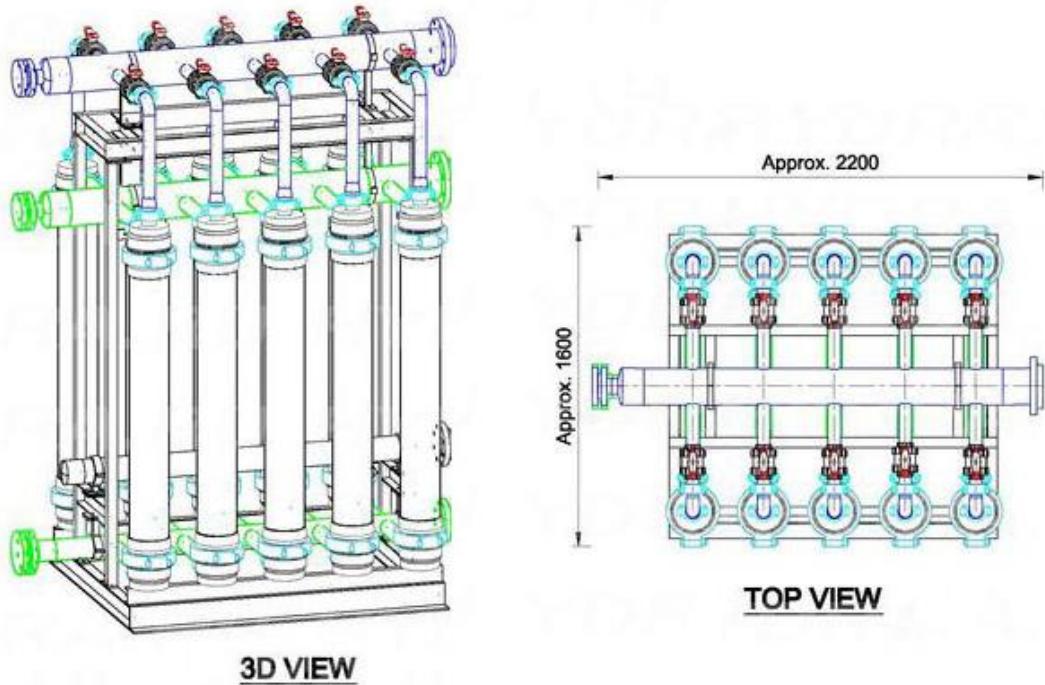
Общий вид и габаритные размеры установки UF 10/4
